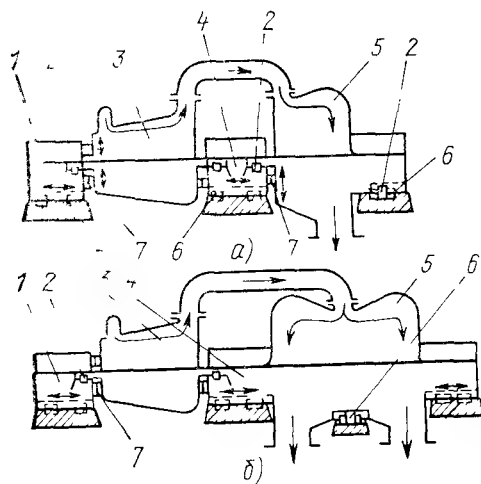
Схема крепления корпусов двухцилиндровых турбин конденсационного типа с однопоточным (а) и двухпоточным (б) ЦНД:
